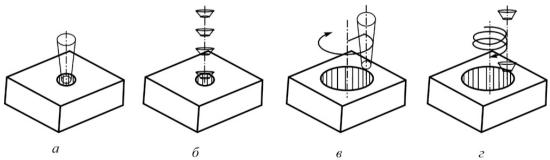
Схемы лазерного сверления: a – прошивка единичным импульсом; δ – импульсная прошивка; ϵ – контурная резка; ϵ – спиральная резка
